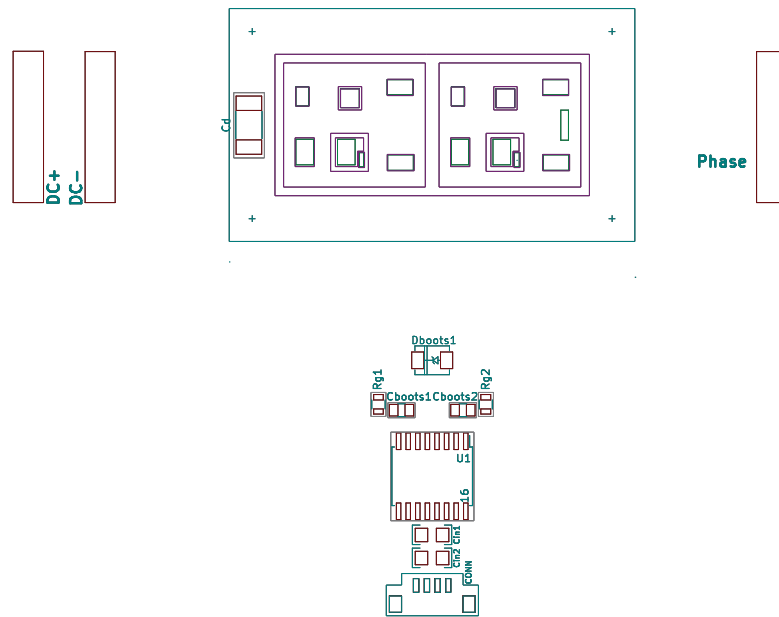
Trilhagem do PCB Flexível – Camada F.B.Silks.
